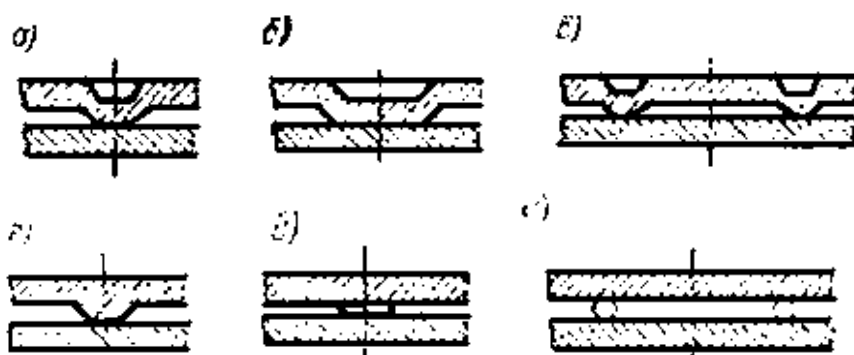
Типы соединений при рельефной сварке внахлестку
